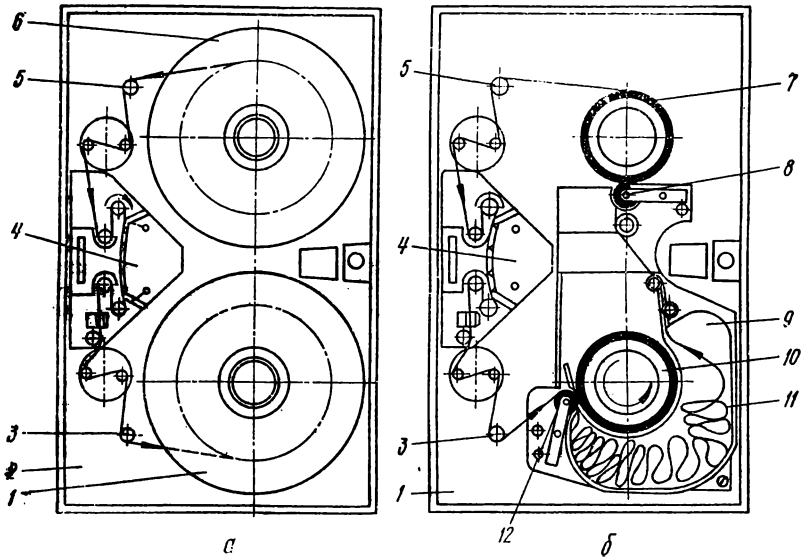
Блочная конструкция МТЛ для двух типоразмеров стандартных катушек
